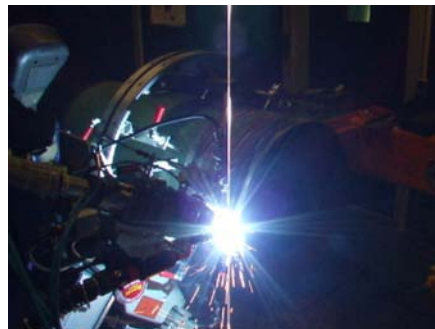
Orbitaltechnik mit Hybridschweißkopf während der Erprobung
